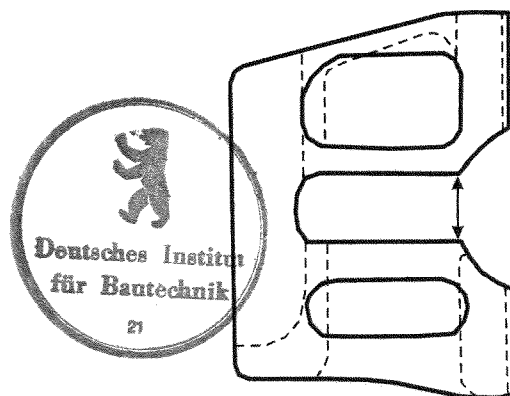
Aufweitversuch für U-Riegel- Anschlussköpfe
